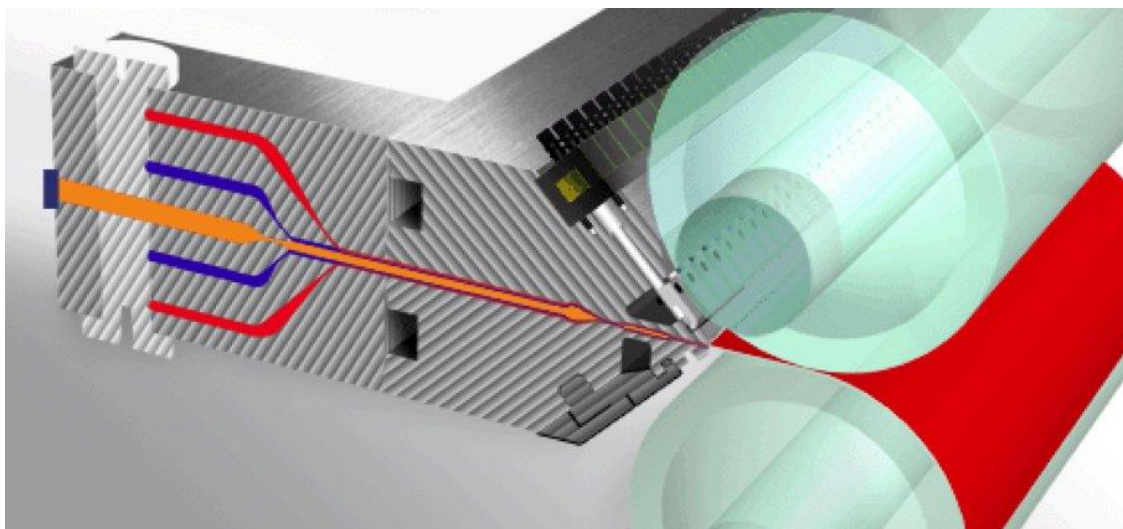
Postrojenje za premazivanje ekstruzijom.
